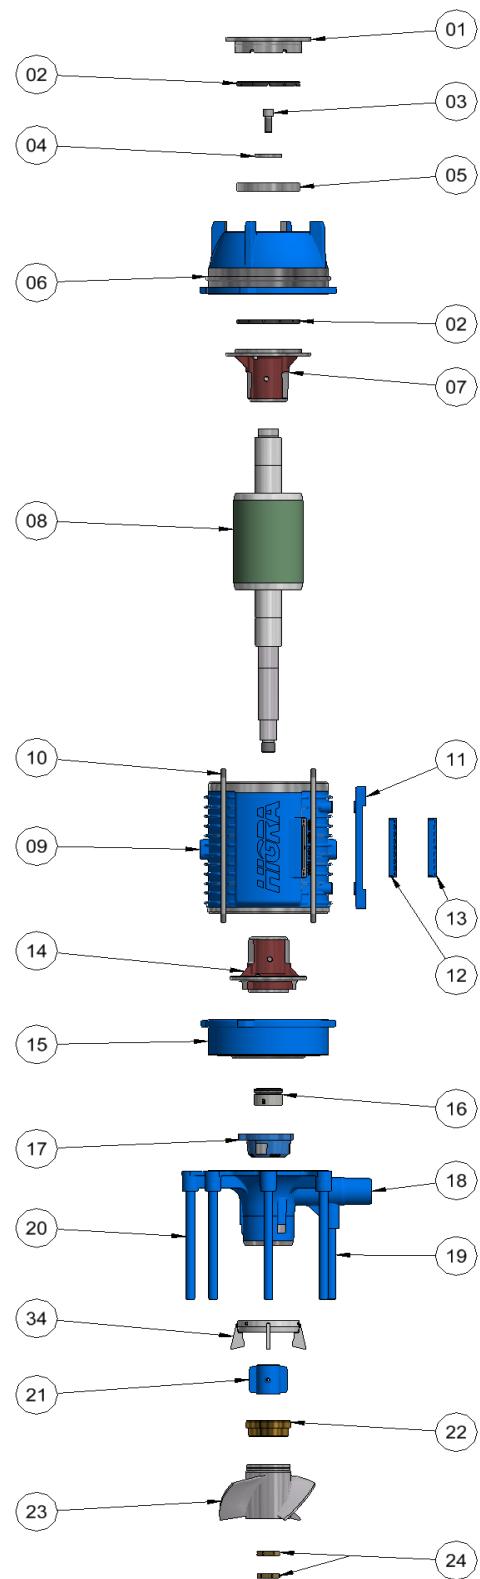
Vista Explodida do Conjunto Motor Tornado.
